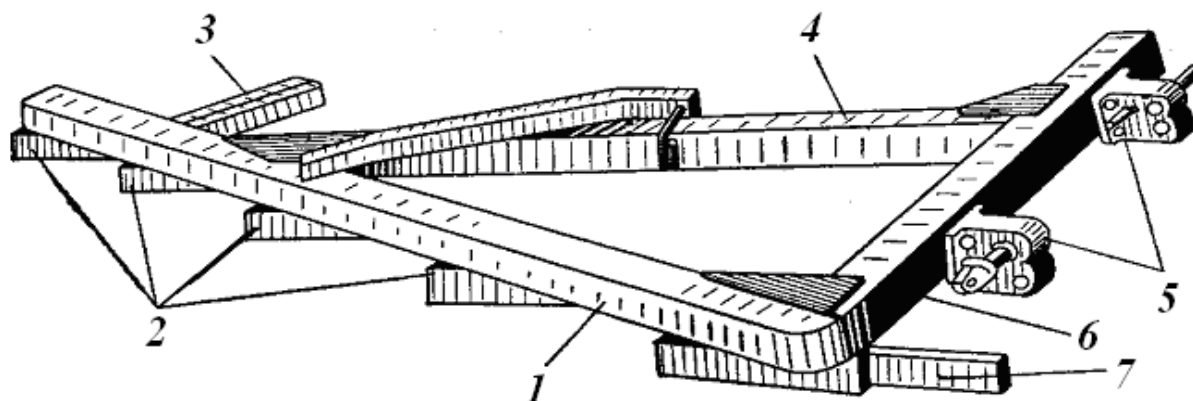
Плоска зварна рама начіпного п'ятикорпусного плуга:
